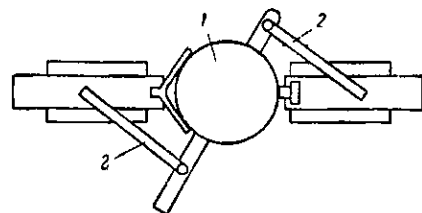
Специальный держатель для контроля децентрировки линз по схеме, изображенной на рис. 75
